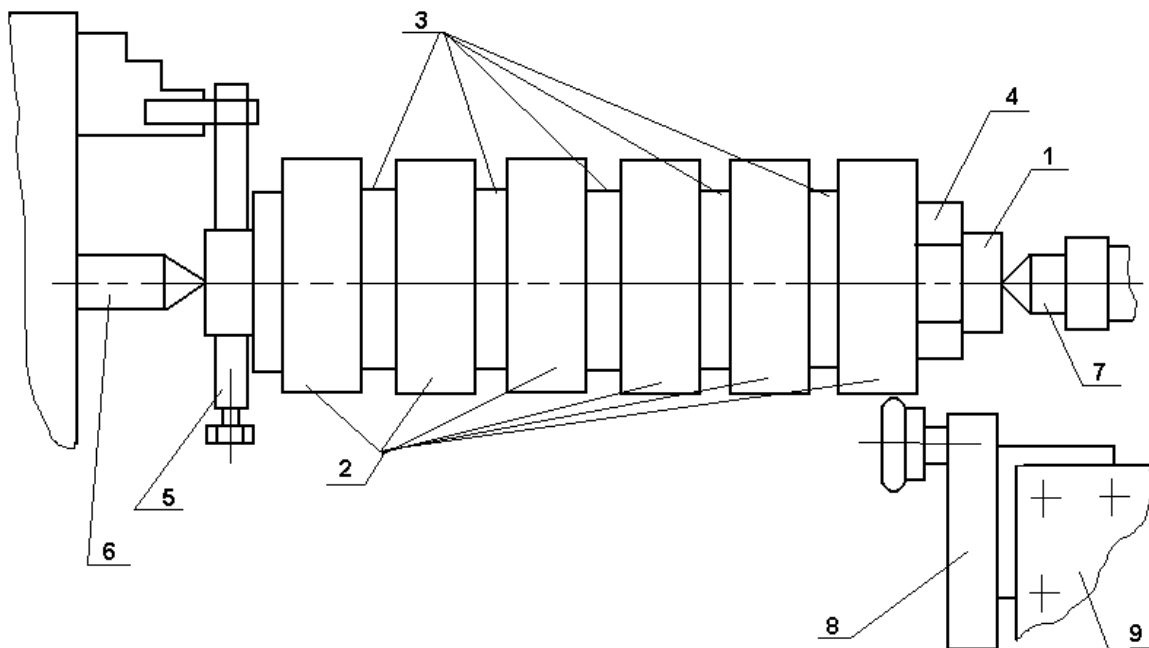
Схема специальной цилиндрической оправки с образцами-кольцами: 1 – оправка; 2 – образцы; 3 – промежуточные кольца; 4 – гайка; 5 – хомут; 6 и 7 – передний и задний центры; 8 – устройство для обкатывания (например роликом); 9 – резцедержатель
